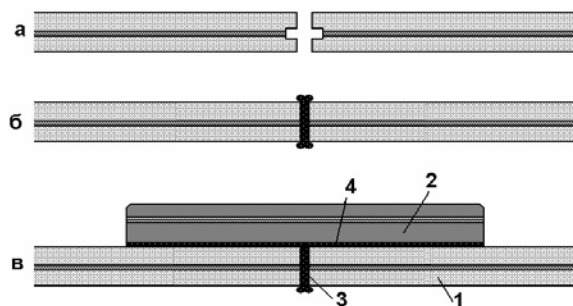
Этапы создания сварного соединения АПТ: а) предварительная выборка концов армировки на торцах труб; б) сварка встык; в) окончательная муфтовая сварка. 1 – АПТ; 2 – электромуфта; 3 – стыковое соединение; 4 – электромуфтовое соединение.
